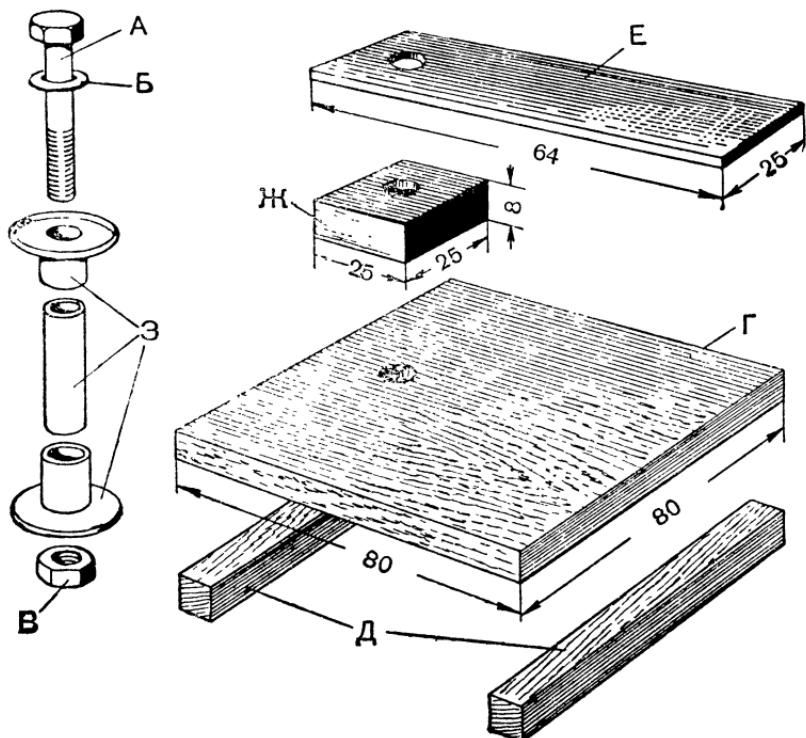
Детали статора № 1 (рис. 7); А — болт; Б — шайба; В — гайка; Г — основание двигателя; Д — подставки; Е — заготовка для башмака статора; Ж — подкладка; З — части каркаса катушки.
